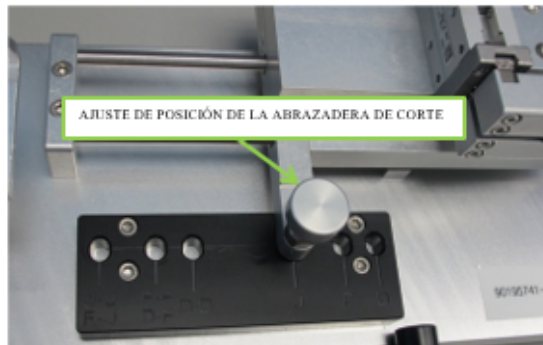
Abrazadera del Corte del cable de acero para el ejercitador Fixture 90195741
